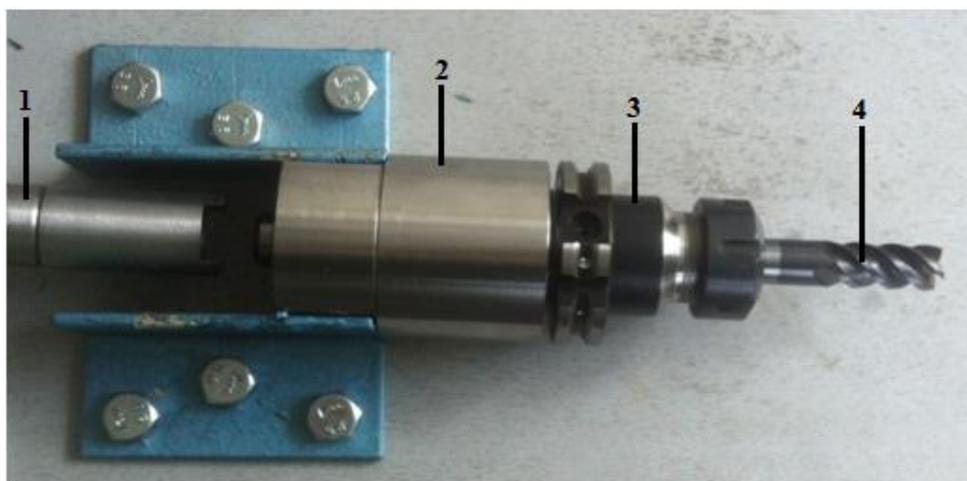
Монтаж захватного болта в цанговом патроне: 1 - ключ; 2 - втулка; 3 - цанговый патрон ; 4 - концевая фреза.
